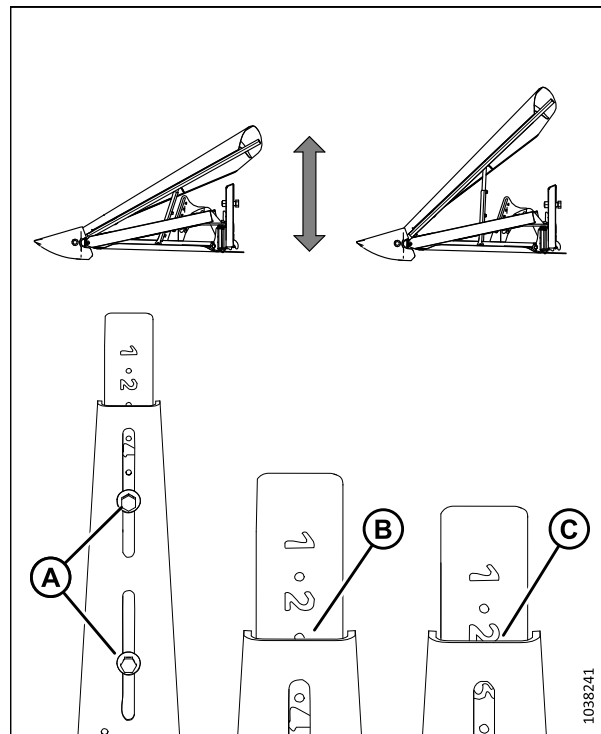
Регулировка высоты верхнего дефлектора
